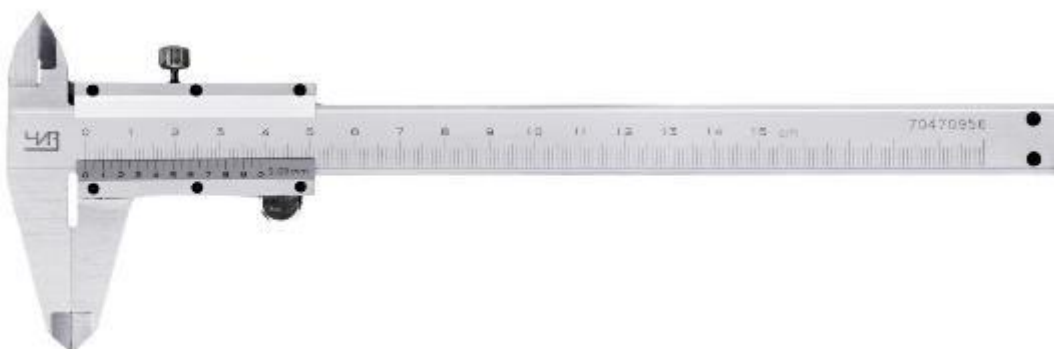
Общий вид штангенциркулей ШЦ-I
